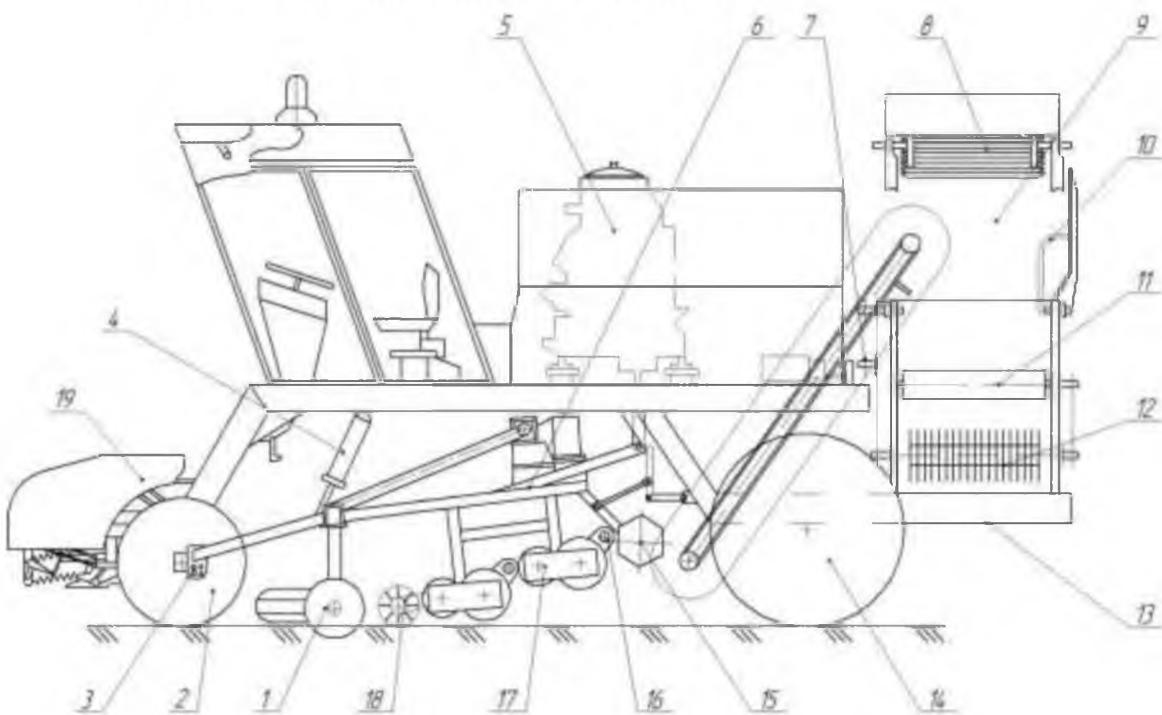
Схема бурякозбирального комбайна з дисковим копачем: 1 – копачі; 2 – передній міст; 3 – штирі регулювання; 4 – гідроциліндр рами; 5 – силовий агрегат; 6 – рама викопувача; 7 – редуктор привода; 8 – навантажувальний елеватор; 9 – бункер; 10 – щиток; 11 – стрічковий транспортер; 12 – грудкоподрібнювач; 13 – основна рама; 14 – міст ведучих коліс; 15 – передаточний бітер; 16 – задній валець; 17 – шнековий очисник; 18 – бітер; 19 – автомат водіння.
